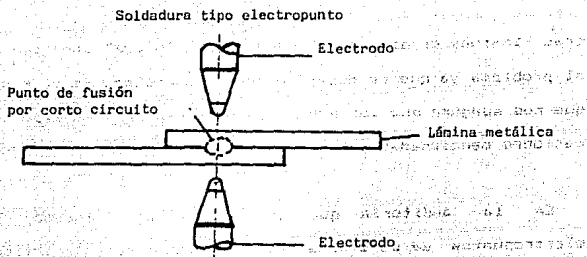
Tipos de soldadura en una carrocería
